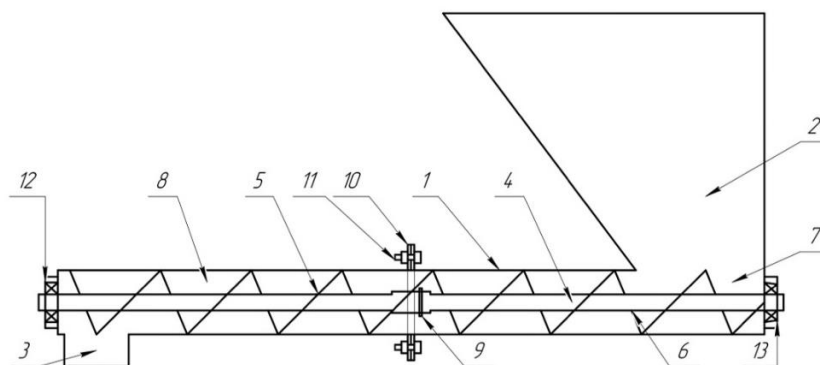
Схематический чертеж смесителя кормов с рабочим органом в виде шнека, оснащенный навивкой циркуляционными отверстиями
